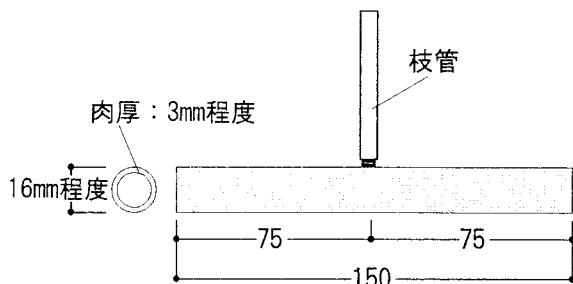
小径竹接合具の形状・寸法 (単位: mm)
